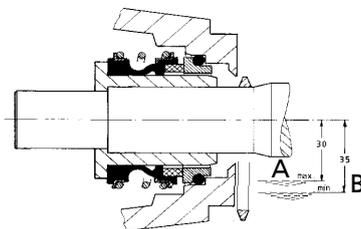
Riempimento della precamera dell'olio - Installazione orizzontale
